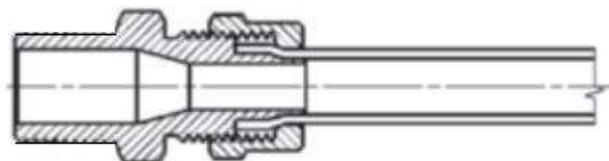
Конструкция и монтаж пневматической трубки в фитинг
